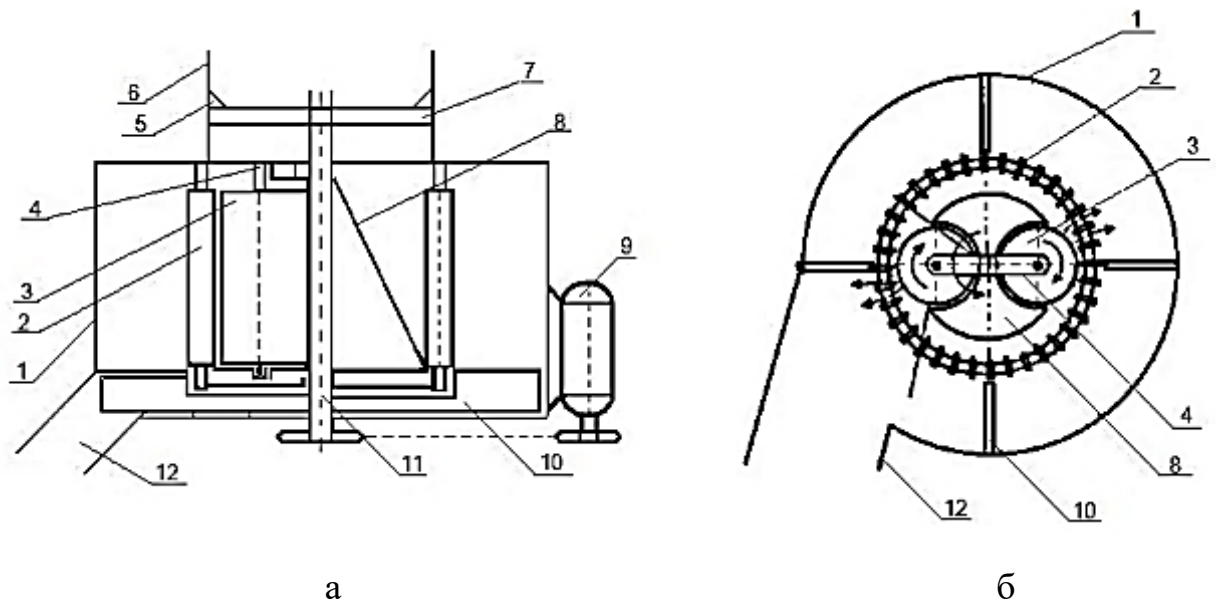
Подрібнювач коренеклубнеплодів з вальцевим підпором: а – загальний вигляд, б – вид А-А 1 – корпус; 2 – ножі; 3 – вальці; 4 – водило; 5 – протиріз; 6 – циліндрична камера; 7 – плоскі ножі; 8 – похилий конус; 9 – електродвигун; 10 - крилач; 11 - вал; 12 - вивантажувальна горловина
